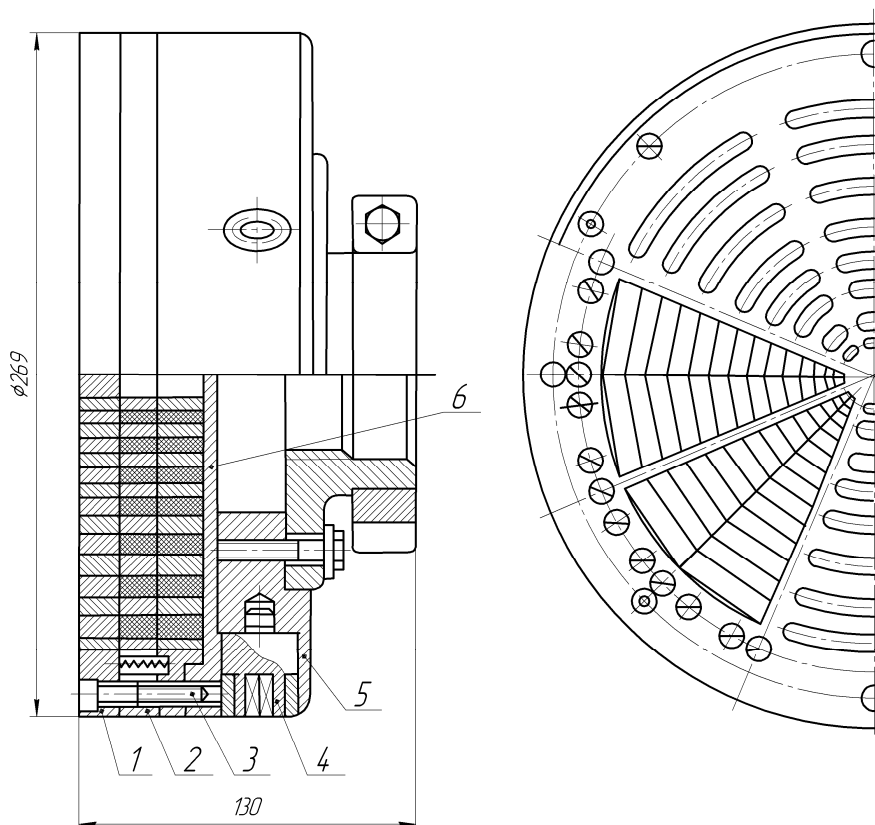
Будова магнітного патрона ПТМ-250: 1 – адаптерна плита; 2 – рухомий блок; 3 – напрямна; 4 – конічне колесо; 5 – корпус; 6 – ведене колесо.
